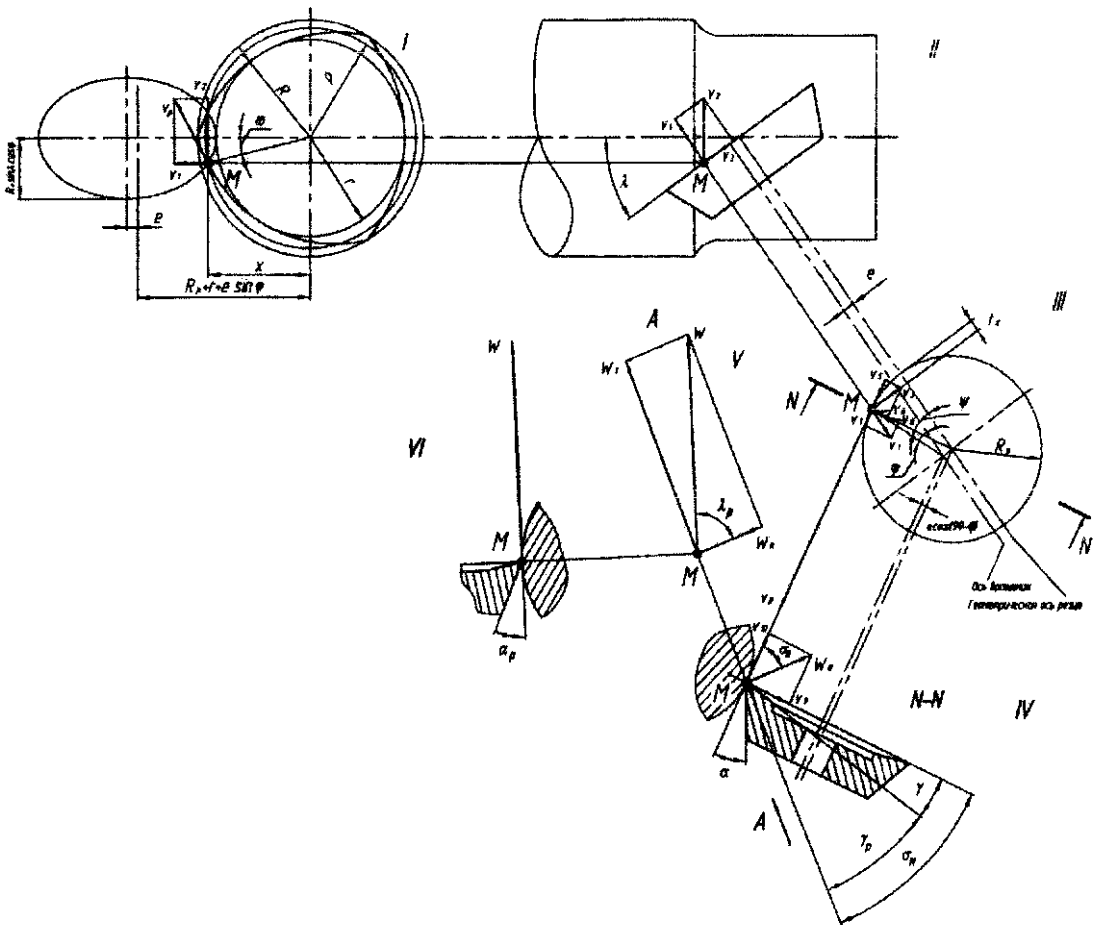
Рабочие углы ротационного резца с передней внутренней конической поверхностью режущей чашки
